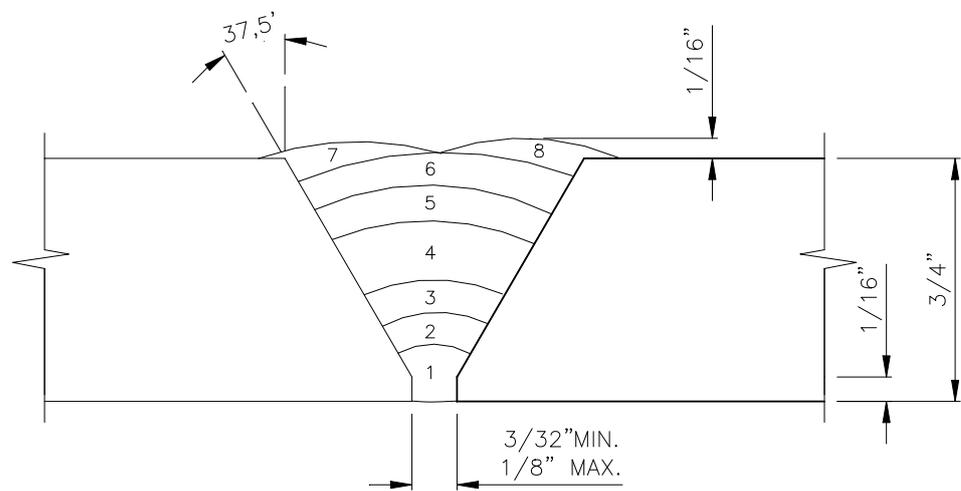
Distribución de pases de soldadura en tubería SCH 80
